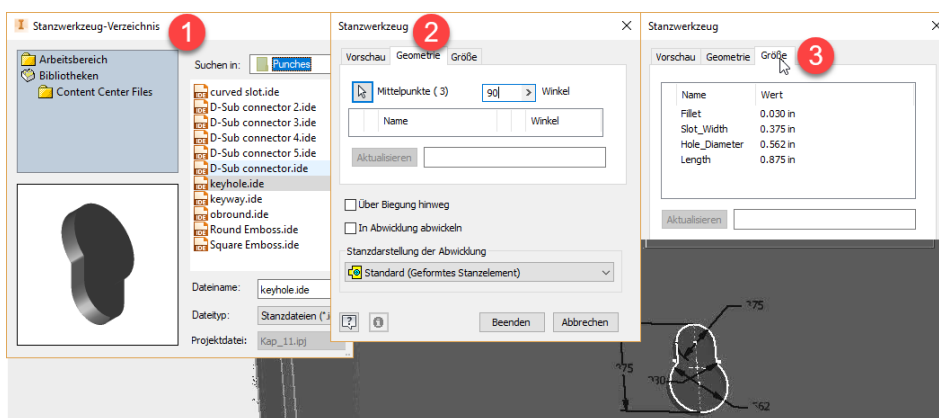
Werkzeug wählen – Punkte wählen – Maße anpassen
